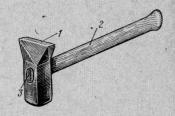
1 — корпус; 2 — ручка: 3 — клин
